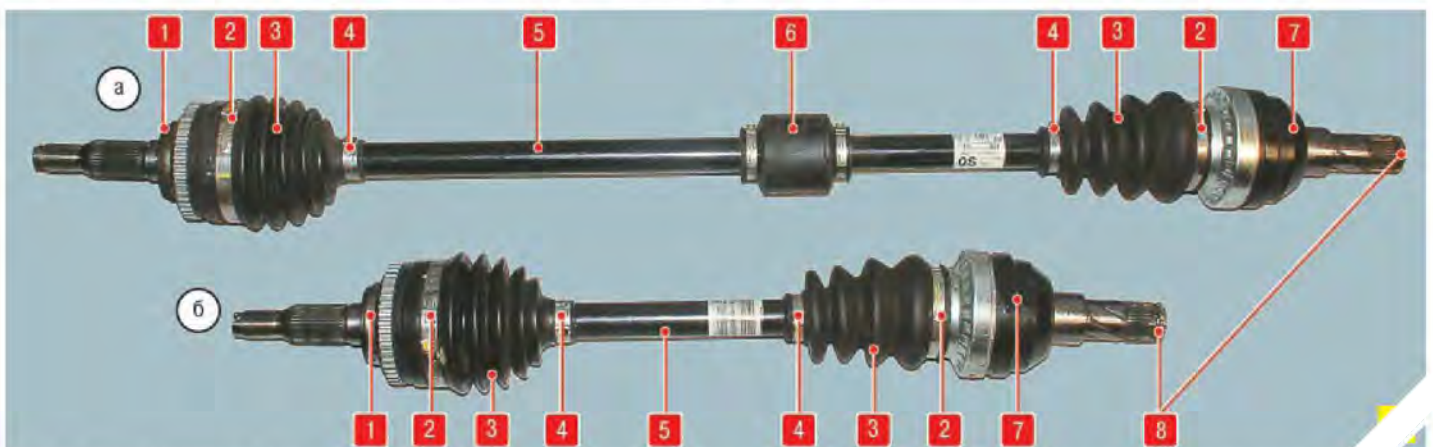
Приводы передних колес: а – привод правого переднего колеса; б – привод левого переднего колеса; 1 – наружный шарнир равных угловых скоростей; 2 – большие хомуты крепления чехлов шарниров; 3 – чехлы шарниров; 4 – малые хомуты крепления чехлов шарниров; 5 – валы приводов; 6 – динамический демпфер; 7 – внутренний шарнир равных угловых скоростей; 8 – стопорные кольца
